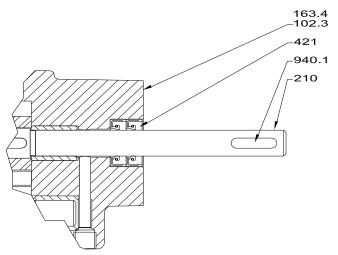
Desenho em Corte bomba FBE c/ retentor
